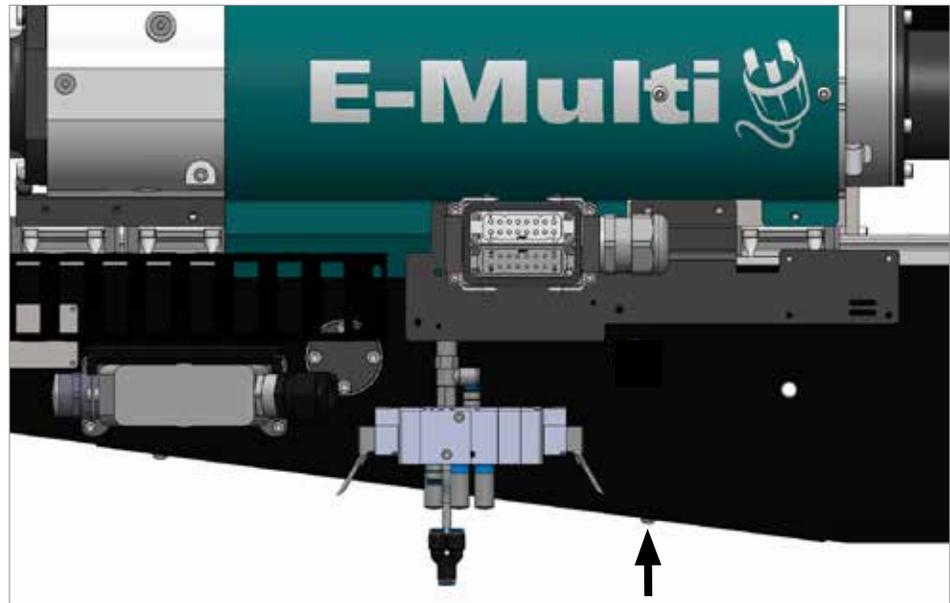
Seitenansicht, die die Position der Schmierpunkte der Kugelgewindespindel des Schlittens zeigt (Systeme vor Mitte 2023)
